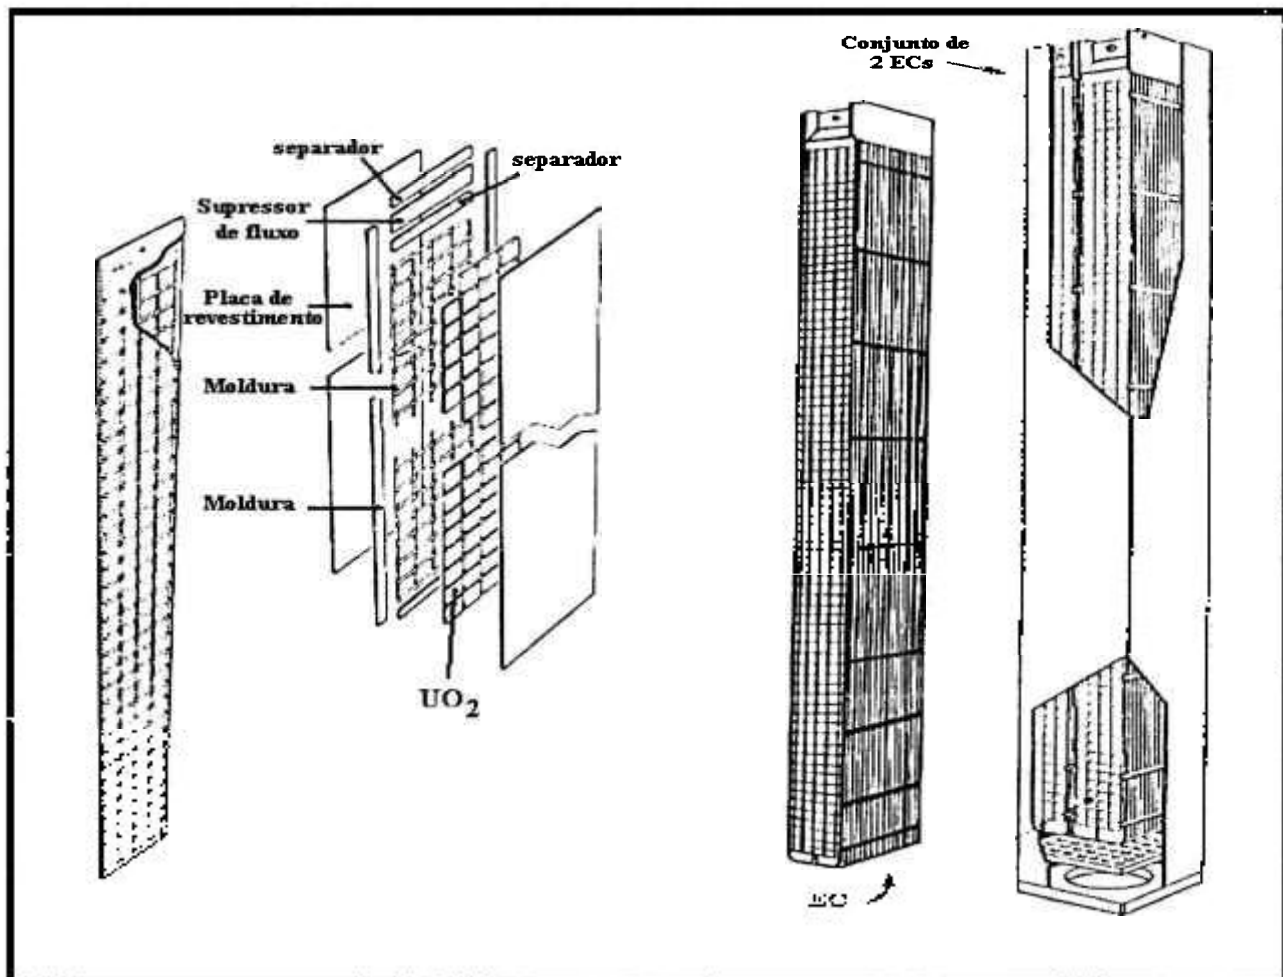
Elemento Combustível tipo Placa para Reator PWR
